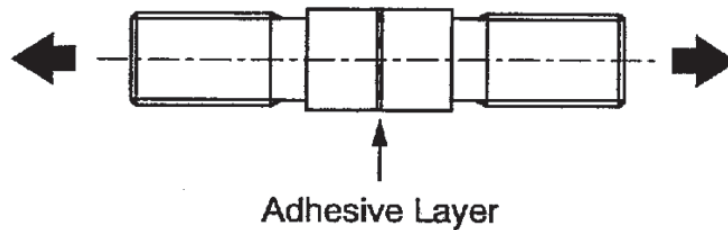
Géométrie : éprouvette butt joint [Yokoyama, 2003]
